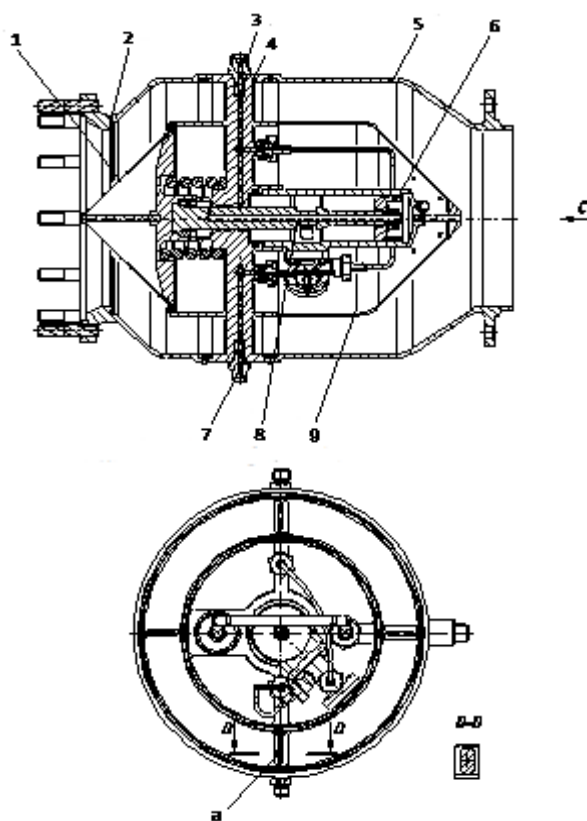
Конструктивно-компоновочная схема разделительного клапана в открытом положении: 1 – затвор; 2, 5 – фланцы (фланец 5 не показан); 3, 9 – штуцеры; 4 – корпус; 6 – поршень; 7 – обтекатель (не показан); 8 – шток, а – ребра
